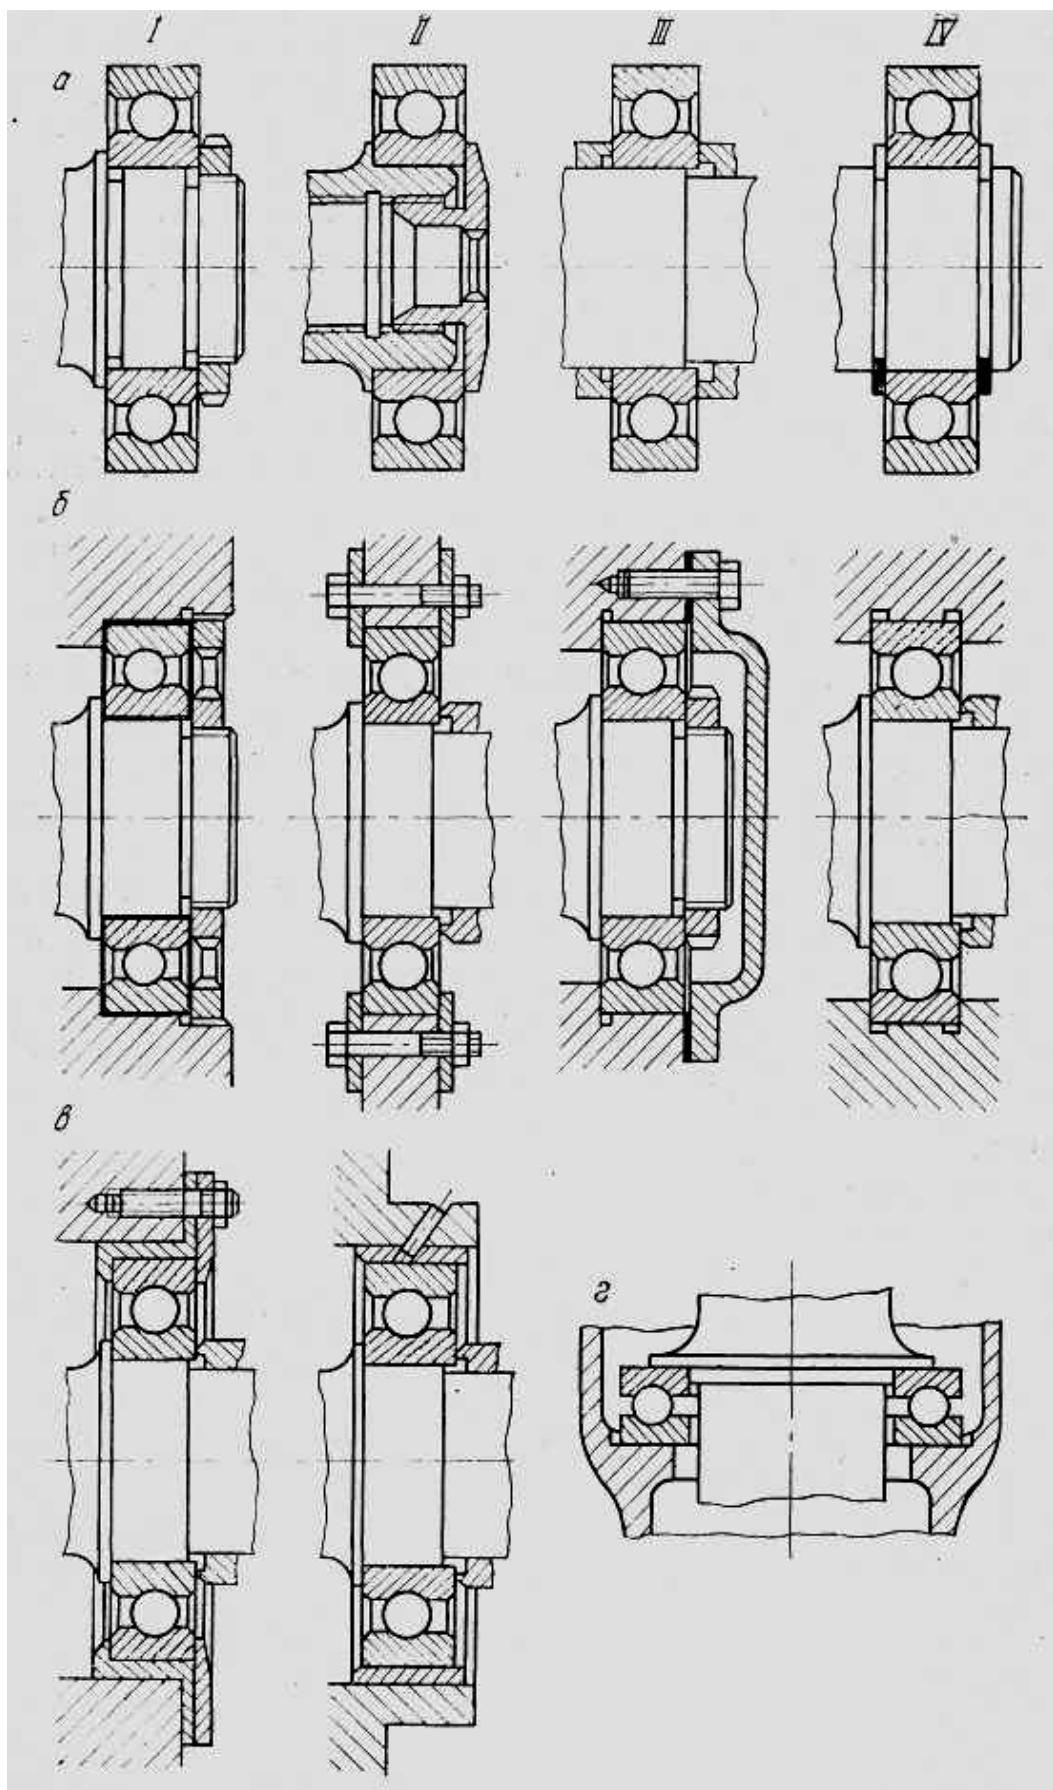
Схемы крепления подшипников при сборке: *a* — радиальных на валах; *b* — радиальных в корпусах; *c* — радиальных на переходных гильзах; *d* — упорных в корпусах
